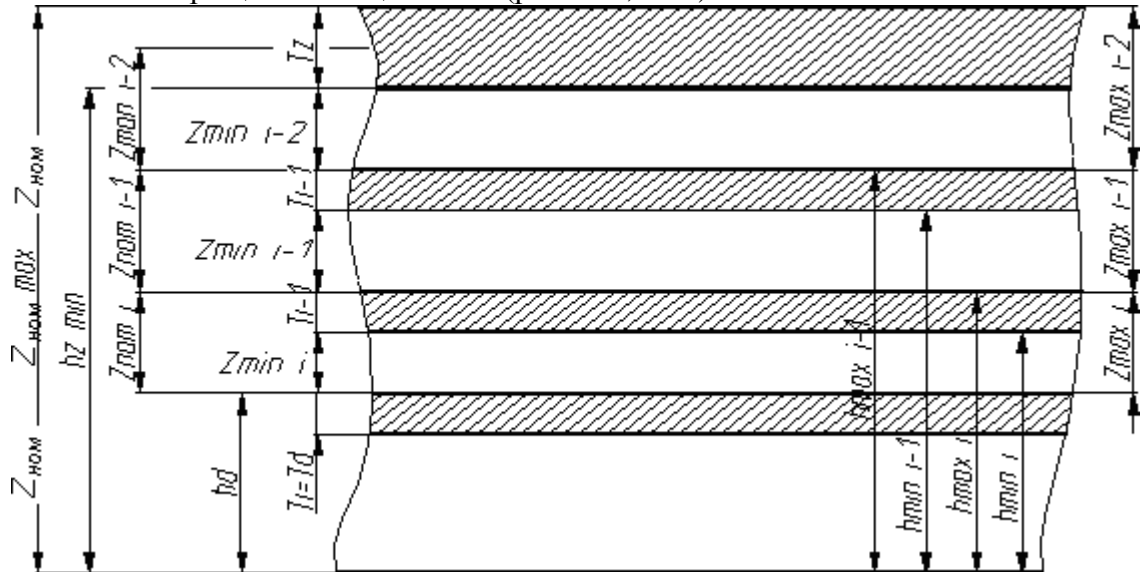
Схема связей между межпереходными размерами, припусками и допусками для охватываемых поверхностей
